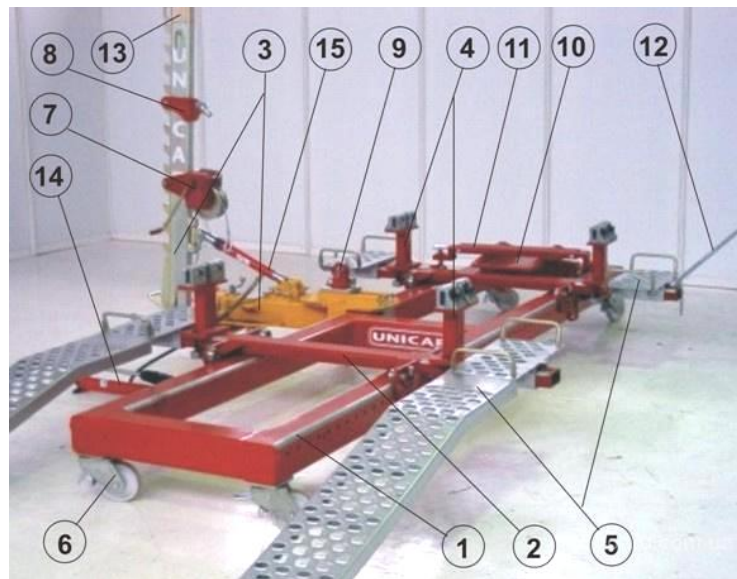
Обладнання для установки кузовів Unicar [15]
